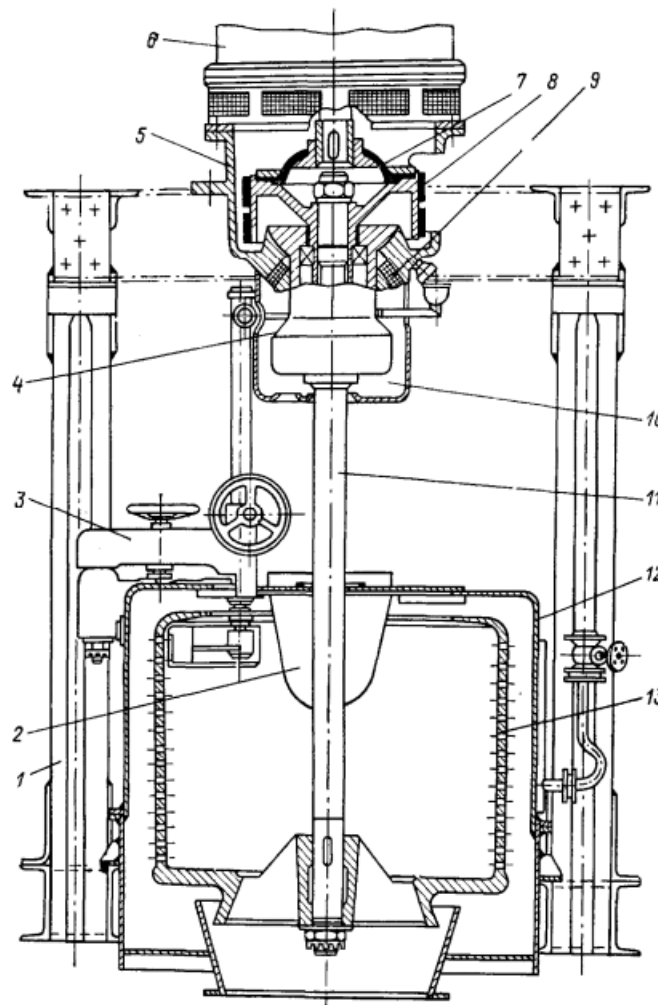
Підвісна центрифуга ФПН 1001У-1: 1 — металоконструкція; 2 — лоток; 3 — механізм зрізування осаду; 4 — корпус підшипників; 5 — корпус приводу; 6 — електродвигун; 7 — муфта; 8 — гальмо; 9 — амортизатор; 10 — привід; 11 — вал; 12 — кожух з кришкою; 13 — ротор
